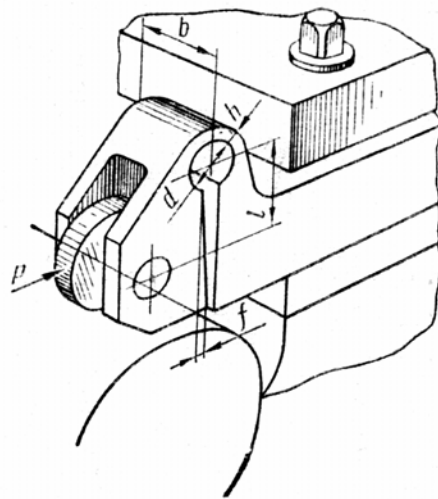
Универсальное однороликовое устройство с пружинящим корпусом
